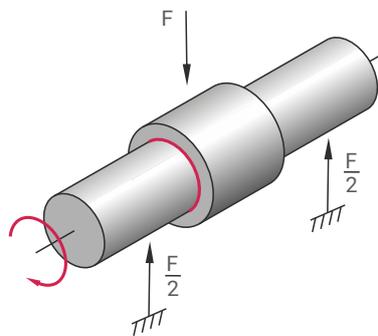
carga vertical constante (no dirección hacia abajo). Cojinete fijo, el árbol gira. El lubricante entra en el área de carga
